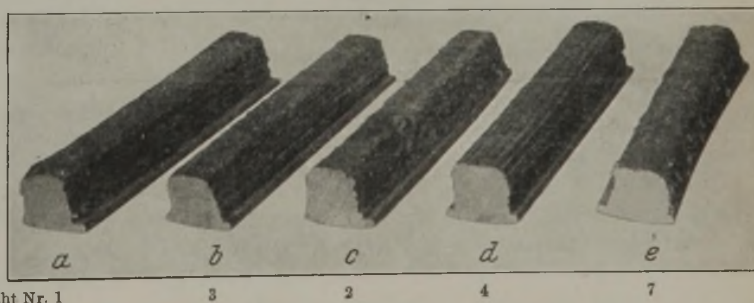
Automatisch lichtbogengeschweißte Barren. 180 A, 16 V, Schweißgeschwindigkeit 15 m/h.
